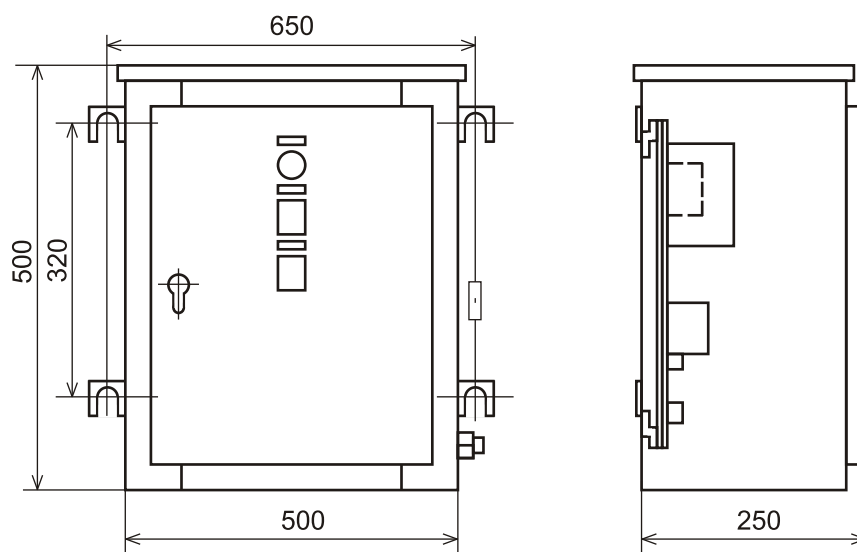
Габаритные и установочные размеры РУСМ
